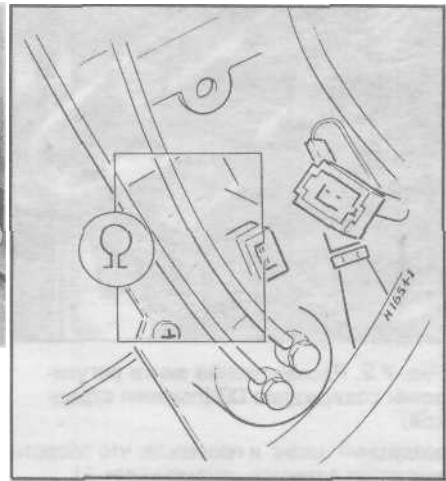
Проверка сопротивления катушки обогревателя клапана прогрева
